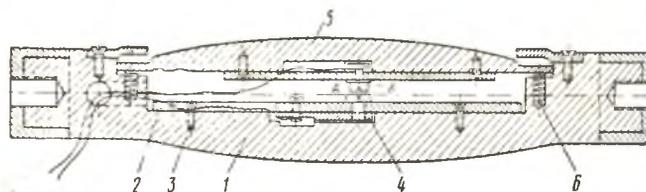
Эскиз рукоятки-выключателя маятниковой пилы
